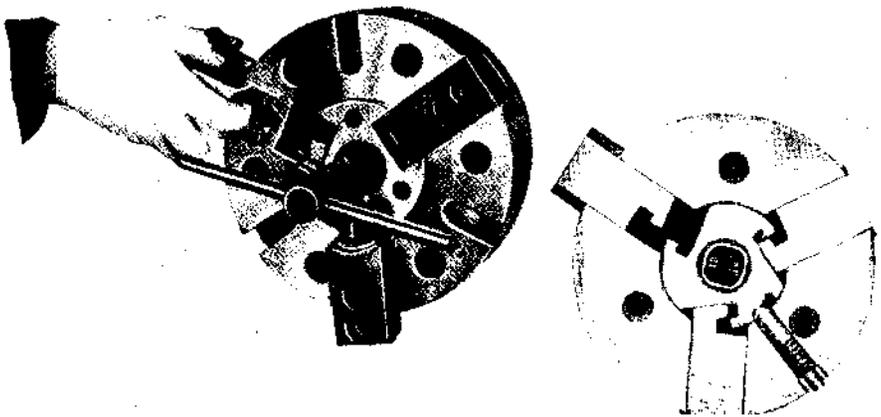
Desmontado de las garras del plato neumático FORKARDT.
